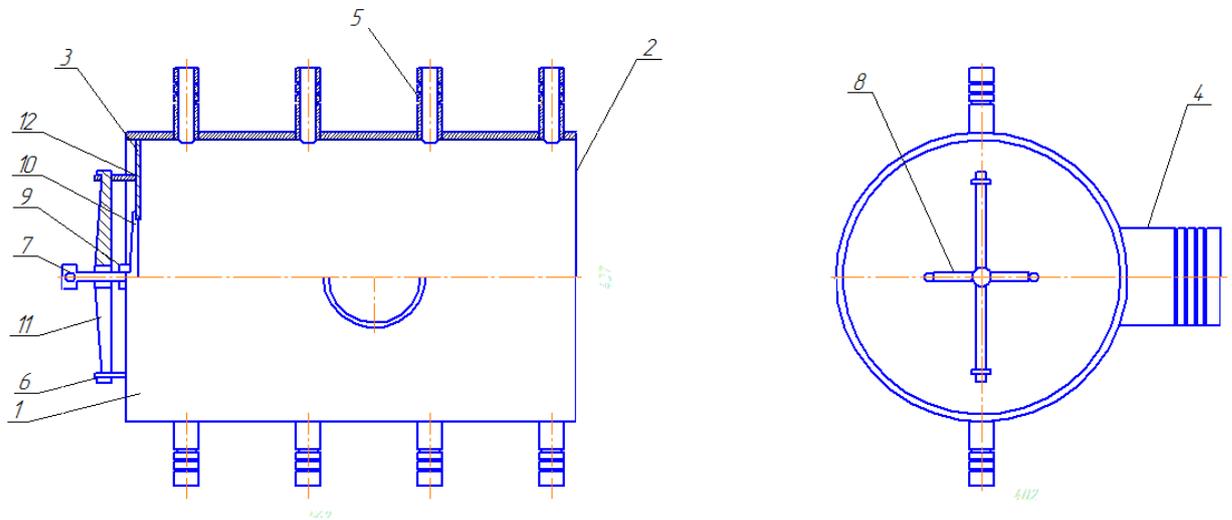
Балон-ресивер: 1 – станина; 2, 3 – бічна частина; 4, 5 – з’єднувальна труба; 6 – затискач; 7 – рукоятка; 8–стакан; 9-кришка; 10-тримач; 11-прокладка; 12 - гайка
